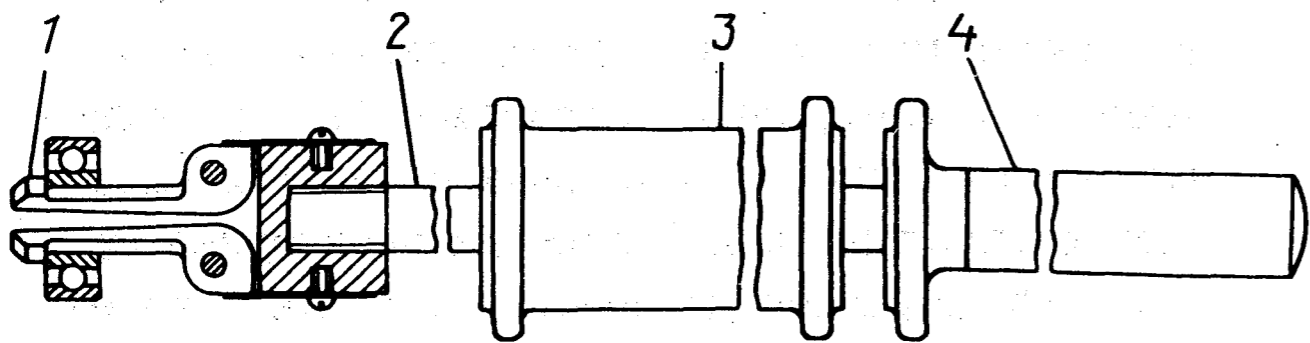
Съемник 7823-6090 для выпрессовки подшипника из коленчатого вала:
